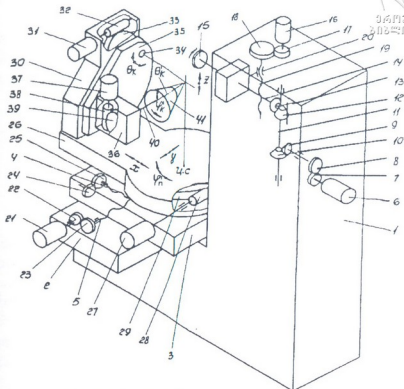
Кинематическая схема зубофрезерного станка с ЧПУ для нарезания некруглых конических колес
